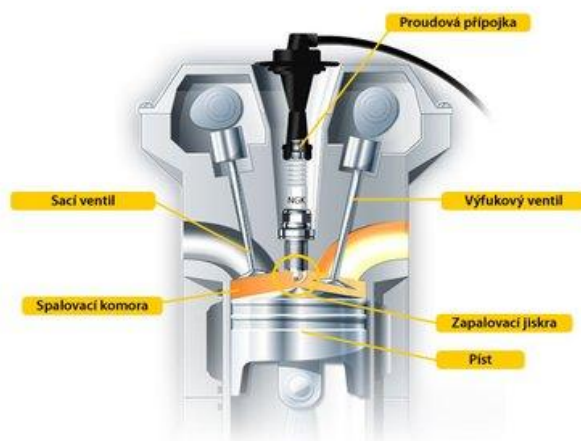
Rozvody motoru, [www.auta5p.eu]
